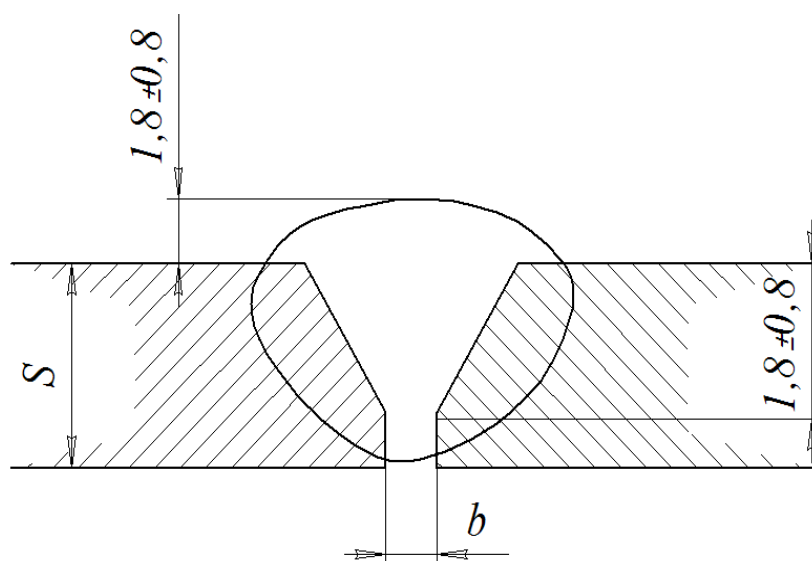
Геометрические размеры сварного стыка
